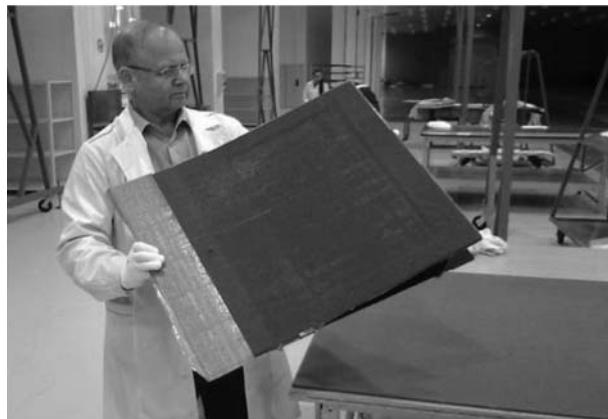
Первая опытная деталь из препрета углепластика марки ВКУ-39
